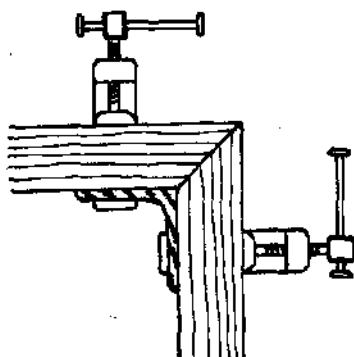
Для изготовления рам можно воспользоваться отрезком стального уголка и струбцинами
